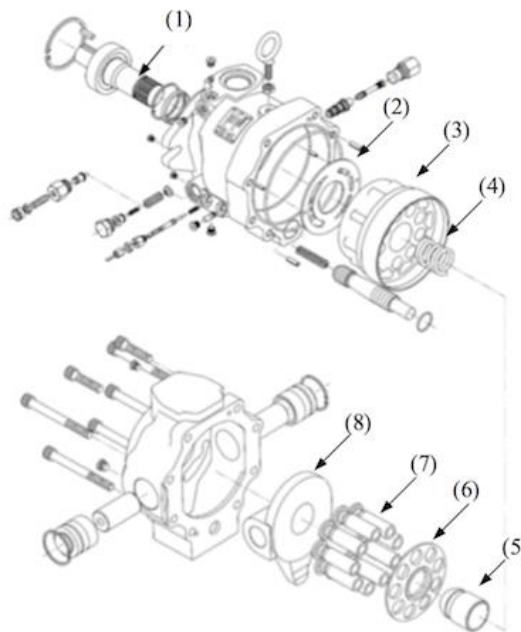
Bomba de pistões em vista explodida. [15]
